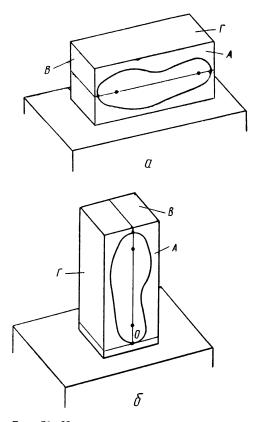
Нанесение на поверхность заготовки: a — контура следа;  $\delta$  — осевой точки начала следа
